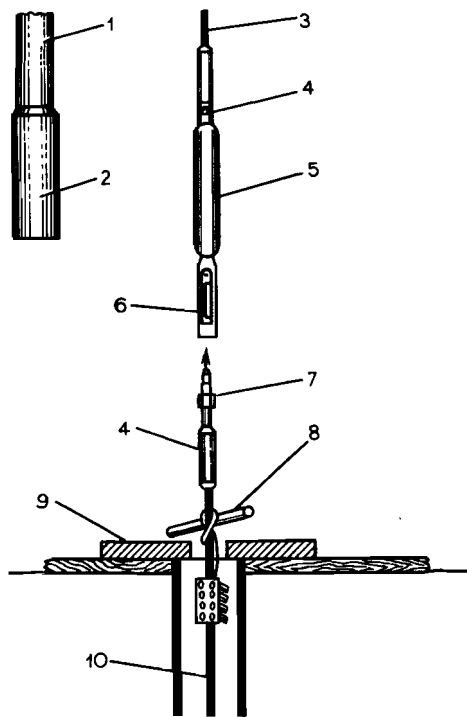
Набор инструментов для спуска труб "поверх" кабеля
